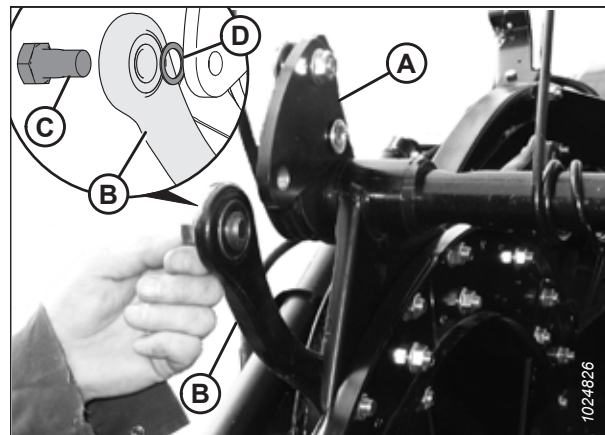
Trou de fixation du levier de la barre et alignement de la biellette
